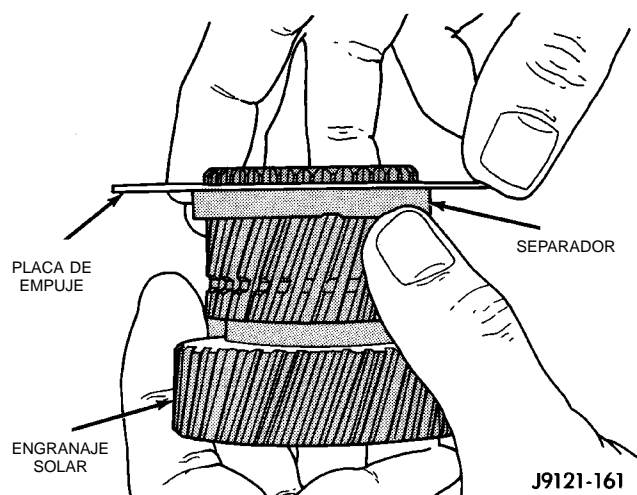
Instalación de la arandela de empuje delantera del casco impulsor en el engranaje solar
